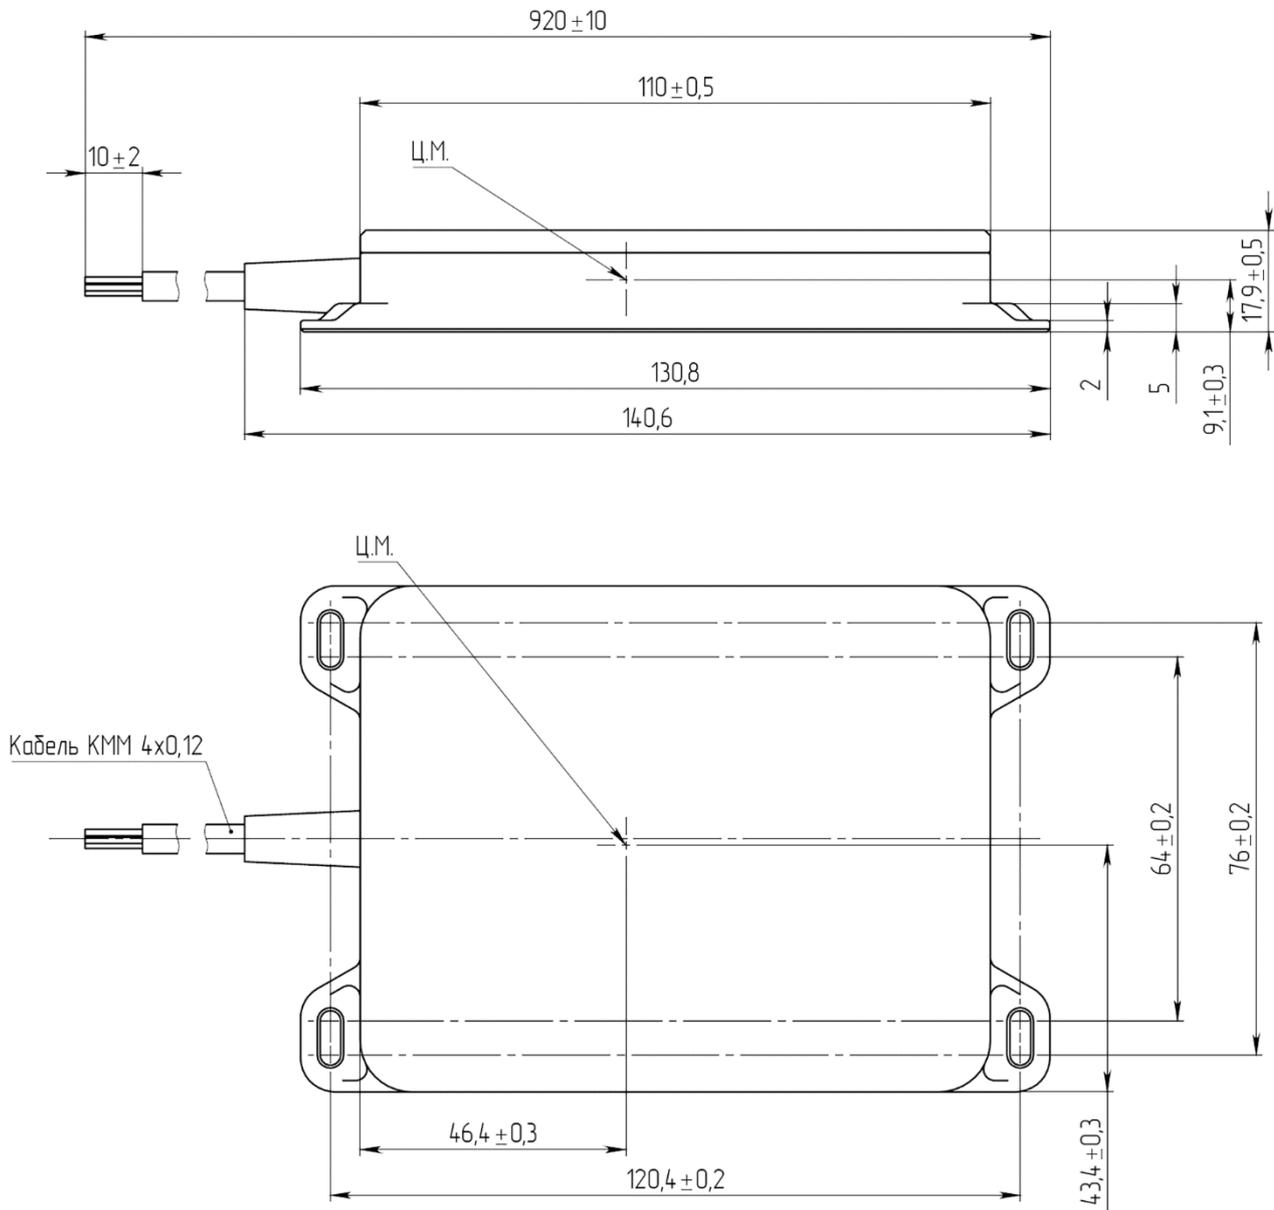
Габаритные размеры изделия, расположение отверстий для крепления
